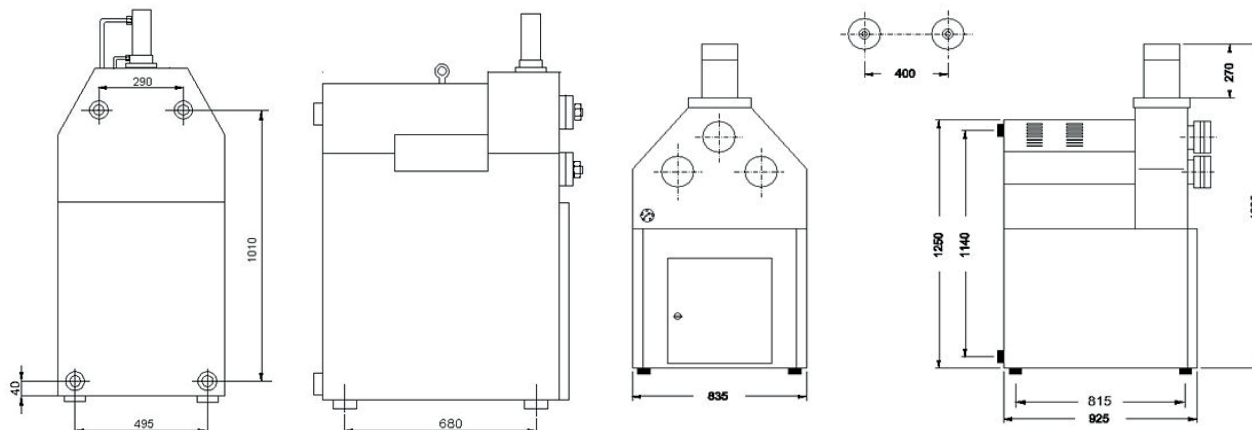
Dimensions PRM 50 FH (à gauche) et PRM 60 FH (à droite)
